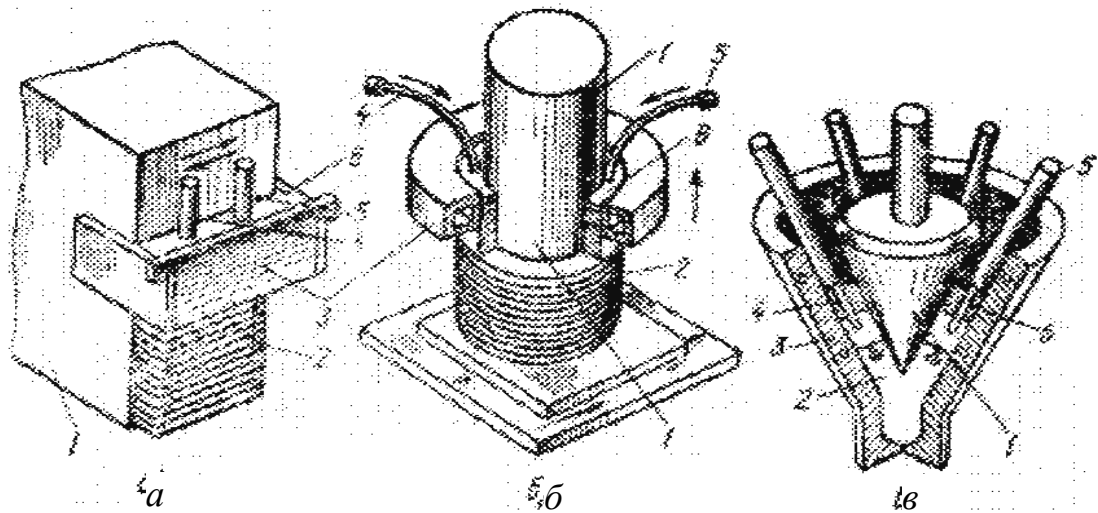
Електрошлакове наплавлення зовнішньої плоскої (а), циліндричної (б) і конічної поверхні (в) дротяним електродом: 1 — електродний дріт; 2 — деталь, що наплавляється; 3 — шлакова ванна; 4 — кристалізатор; 5 — наплавлений шар; 6 — зварювальна ванна
